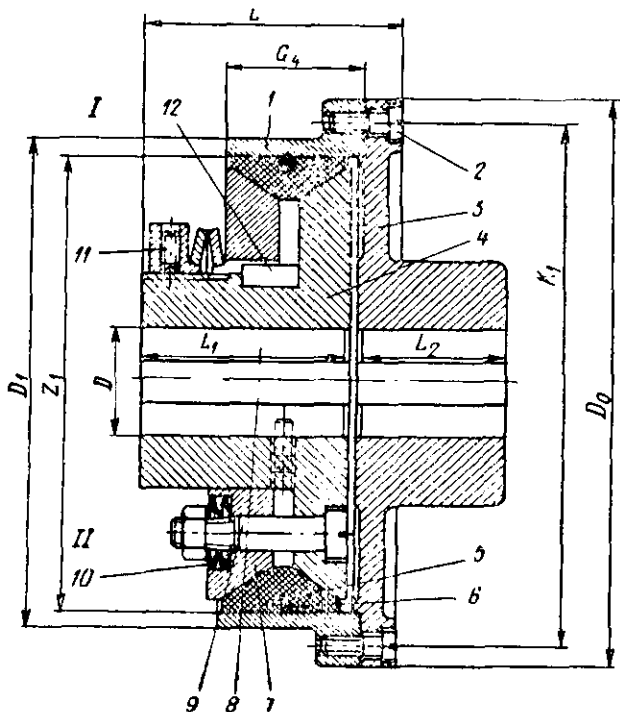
Муфта с рабочими поверхностями в форме конуса и цилиндра
